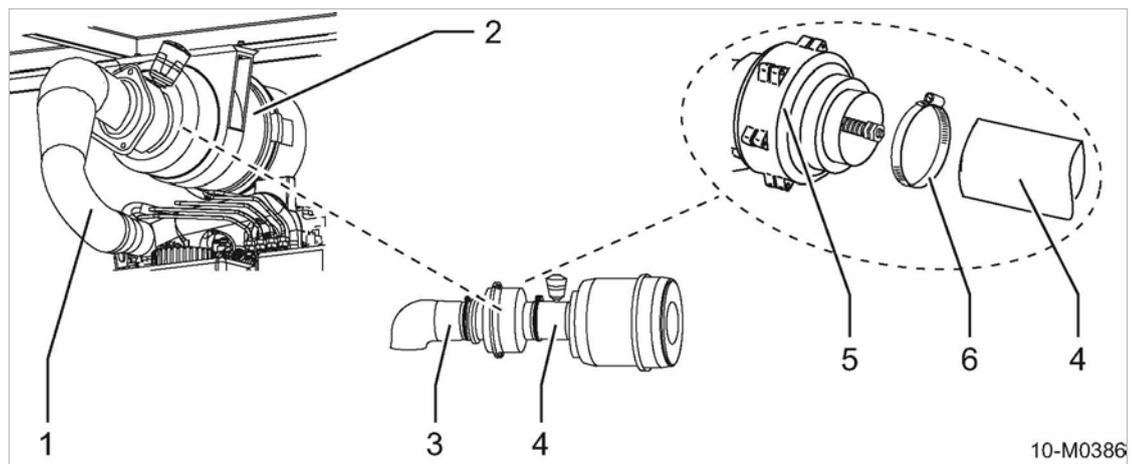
Válvula de cierre de entrada de aire del motor mantenimiento
